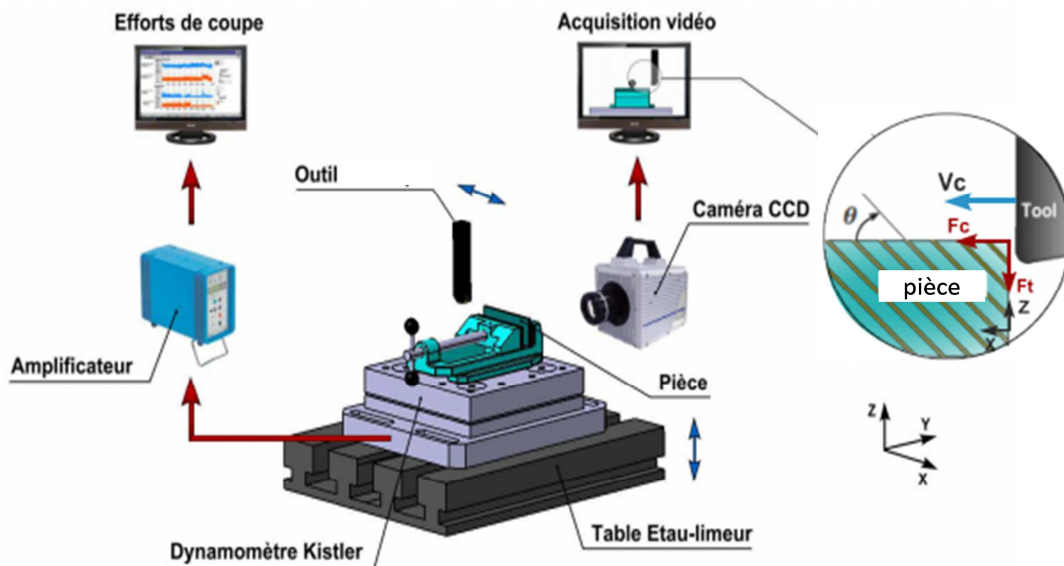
Dispositif instrumenté pour essai tribologique et essai de coupe orthogonale.
